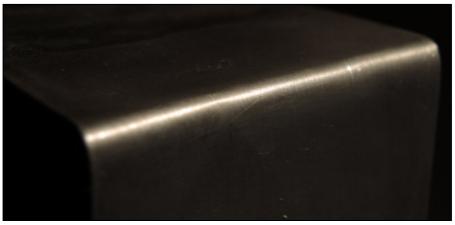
Abkantungsradius eines Aluminiumbleches
